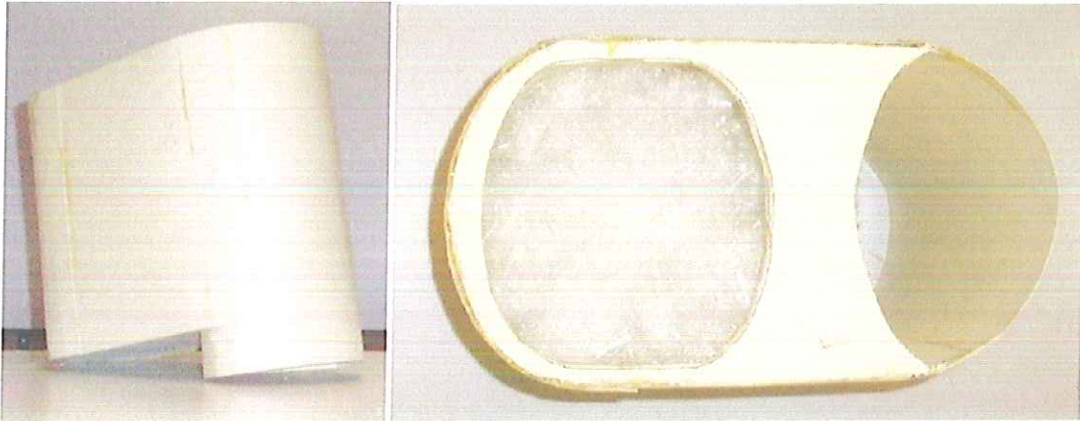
Version Final De La Tolva Empacadora, Vista Posterior
